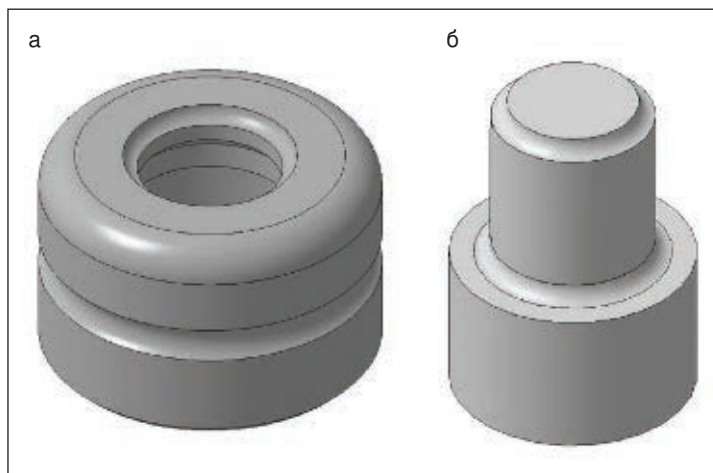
Заготовки штампа до наплавки: а — заготовка матрицы; б — заготовка пуансона
